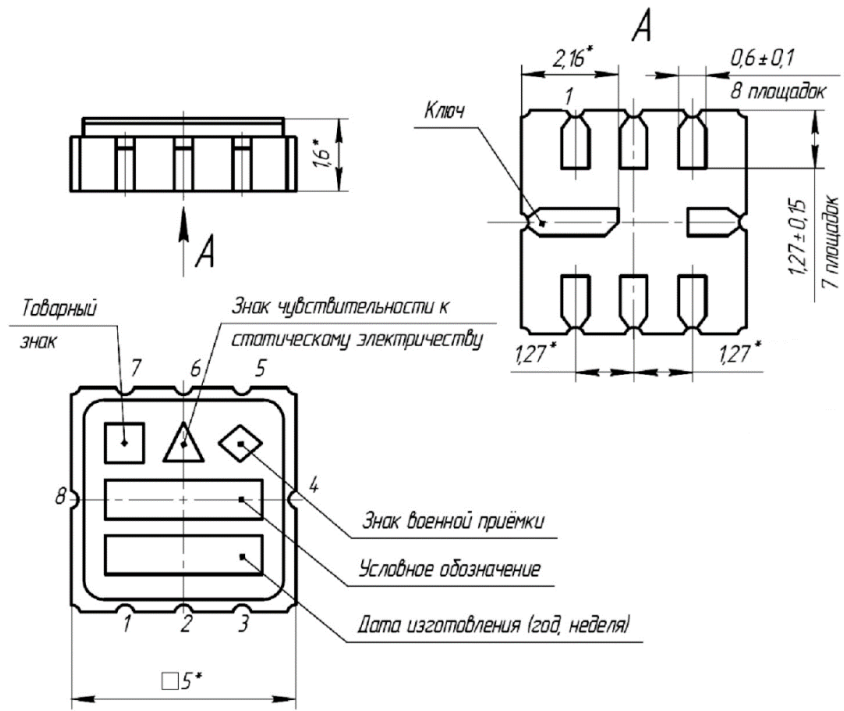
Внешний вид корпуса 5140.8-АНЗ
